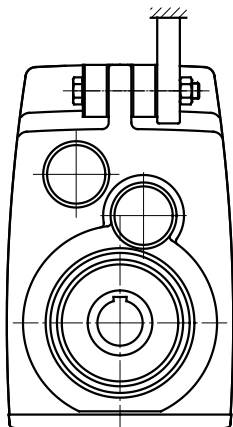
Motorreductor op as zonder installatiesteun met bevestigingselement gemonteerd
